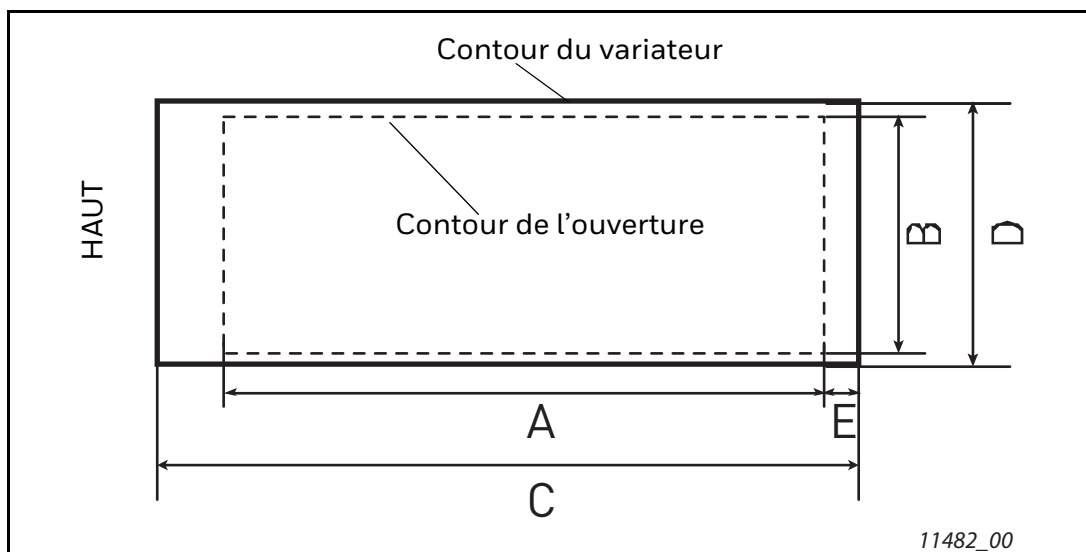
Dimensions de découpe de la bride pour châssis MR7 à MR9
